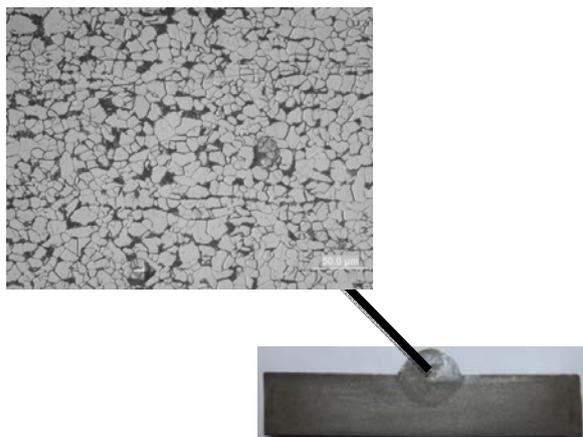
Структура сварного шва сварка в среде углекислого газа без применения модификаторов
